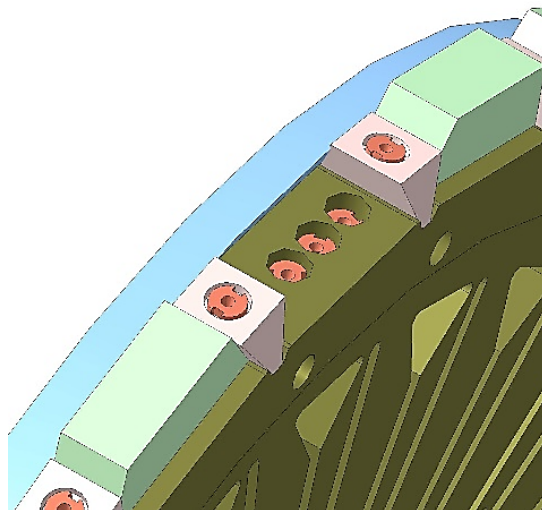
Установка кавитаторов в корпусе сборного круга.
